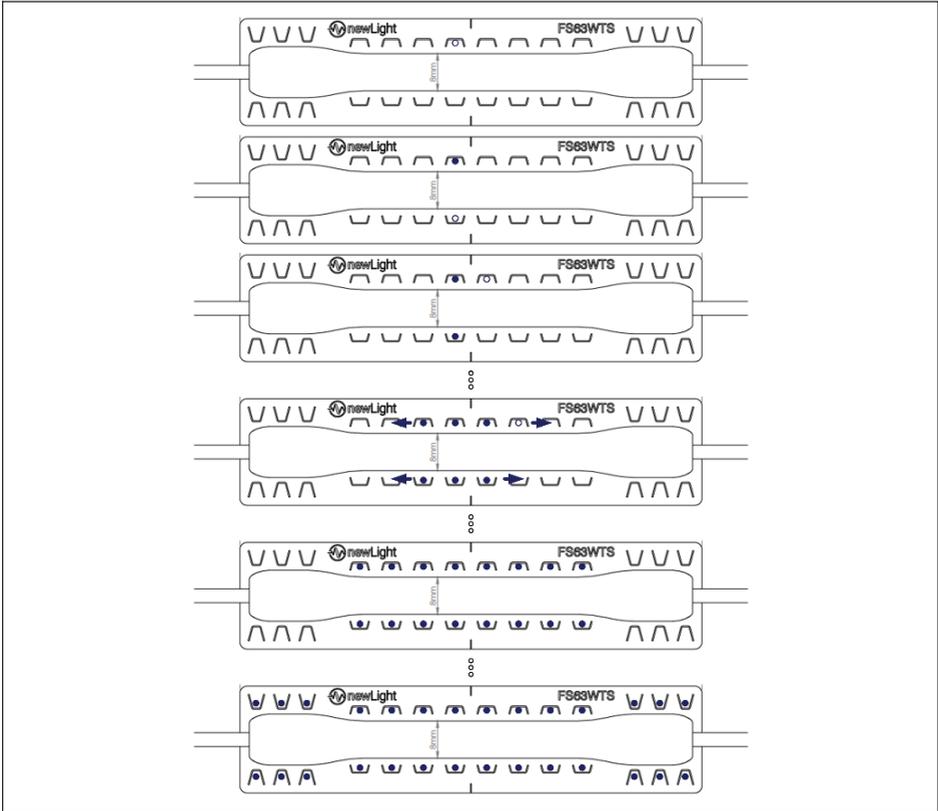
Schweißreihenfolge für FS63WTS
